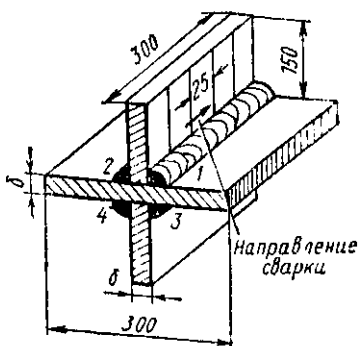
Крестовая проба (1 — 4 — порядок сварки швов)
